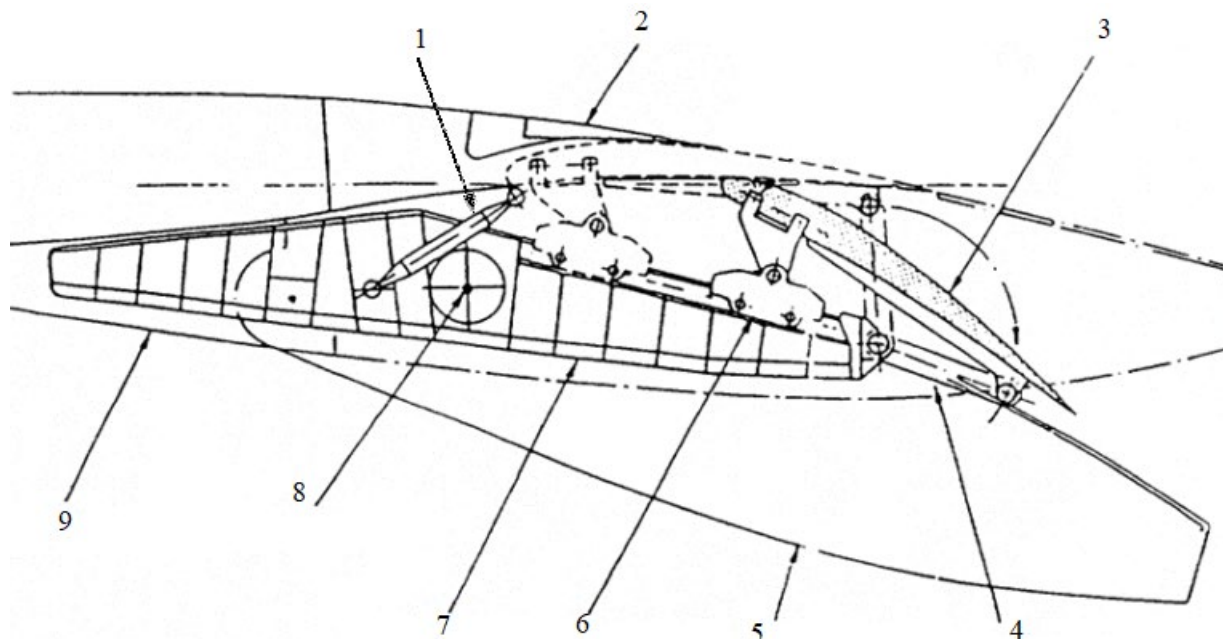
Схема опорного пристрою закрилків: 1 – привідна ланка; 2 – спойлер; 3 – закрилок; 4 – задня ланка; 5 – рухома частина обшивки; 6 – каретка; 7 – напрямна балка; 8 – обертальний силовий привід; 9 – нерухома частина обшивки
